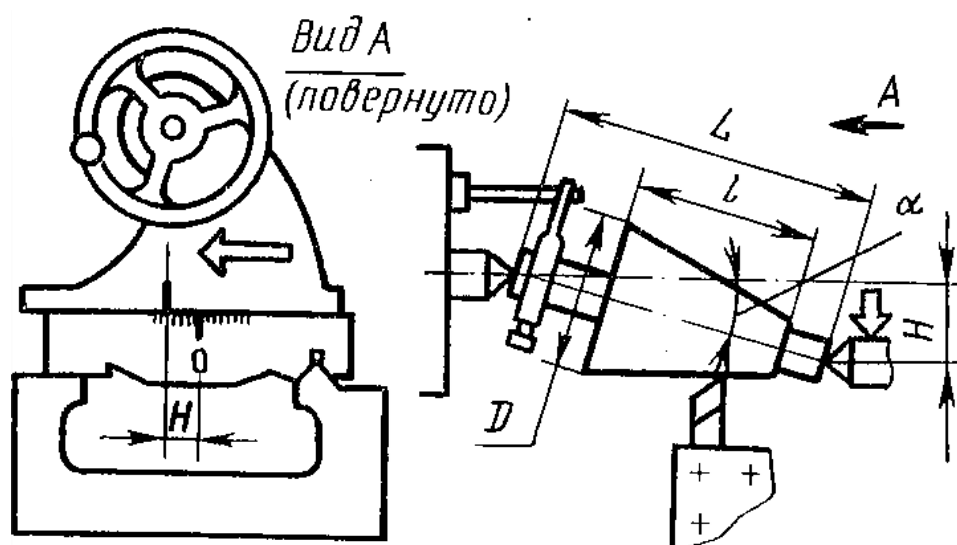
Схема точения конической поверхности смещением корпуса задней бабки
